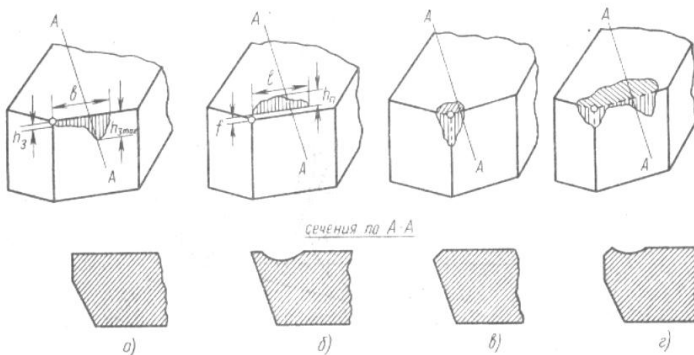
Износ режущего лезвия резца, изготовленного из быстрорежущей стали: а-неравномерный износ по задней поверхности; б- образование лунки на передней поверхности; в-износ вершины резца; г- одновременный износ по задней и передней поверхностям лезвия резца
